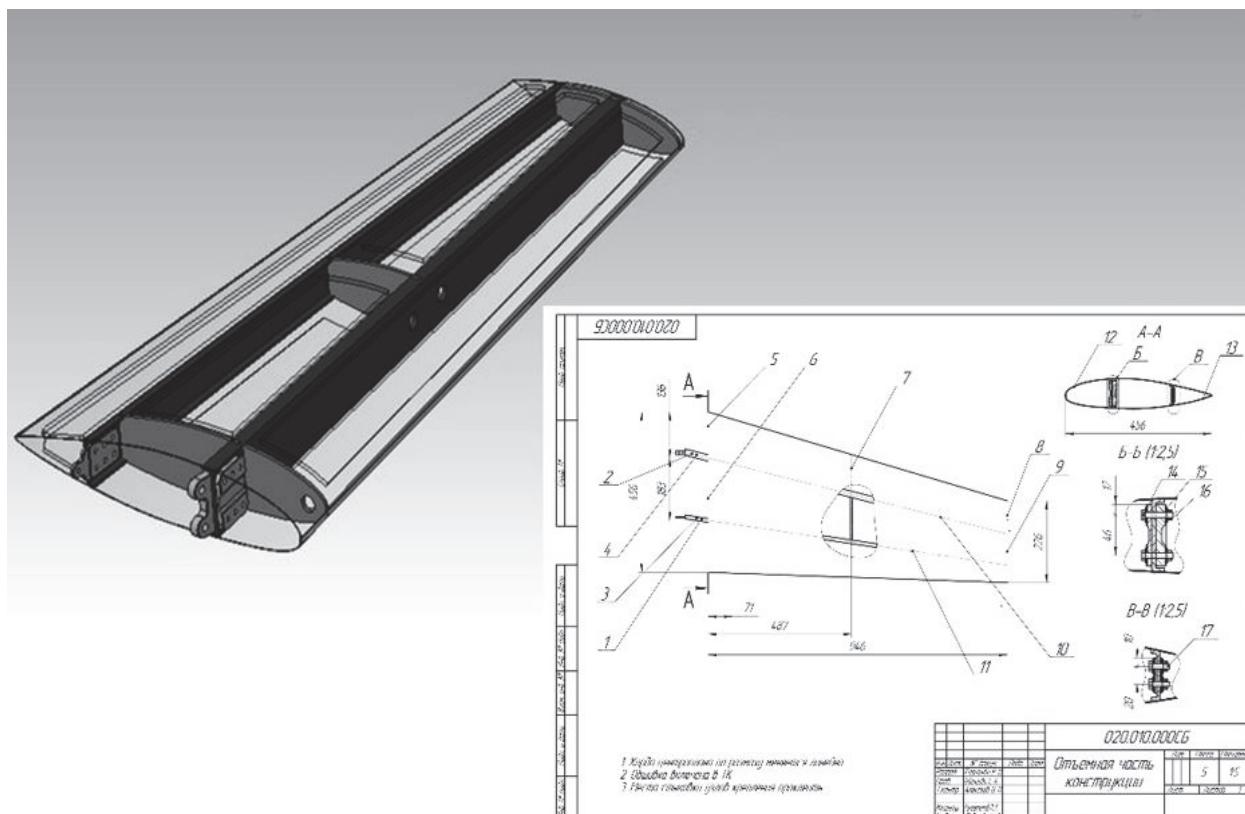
Сборочный чертеж и 3D-модель отъемной части крыла
